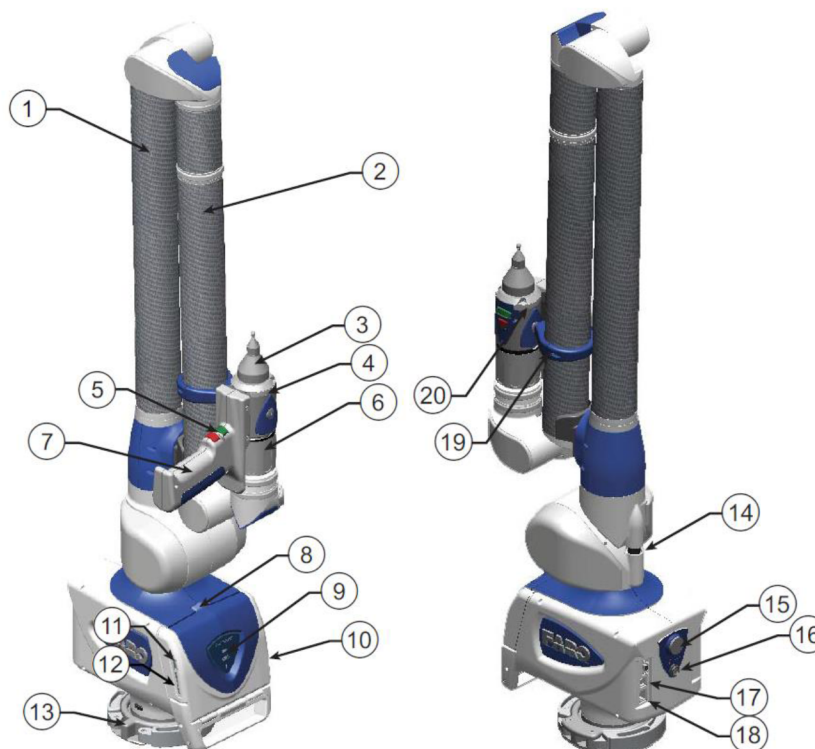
Mobilní souřadnicový měřicí stroj FaroArm Quantum M [2]
